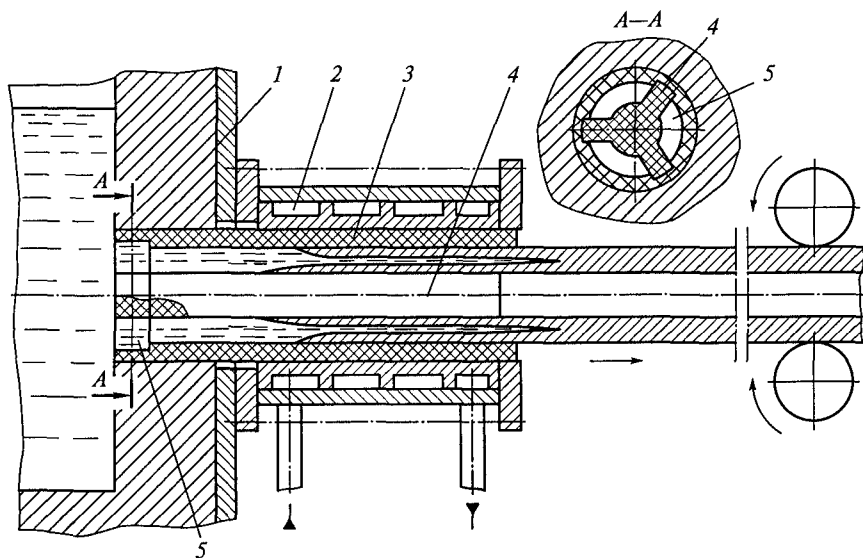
Схема кристаллизатора для горизонтального непрерывного литья трубчатых заготовок и профилей:
